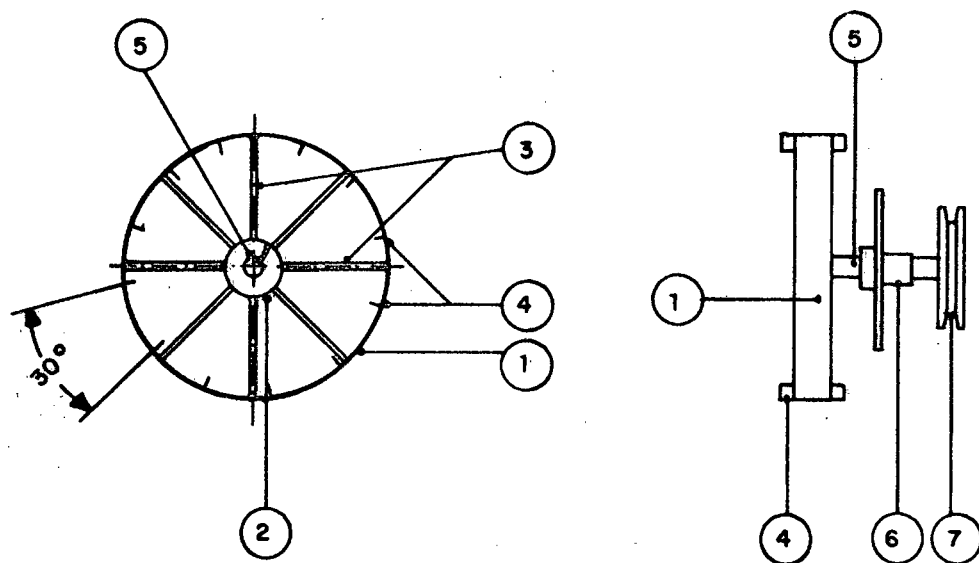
Vistas lateral e frontal da roda tratora.
